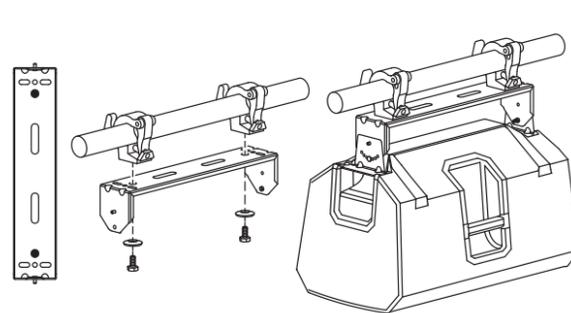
Montagem horizontal usando braçadeiras de treliça TCA-1
